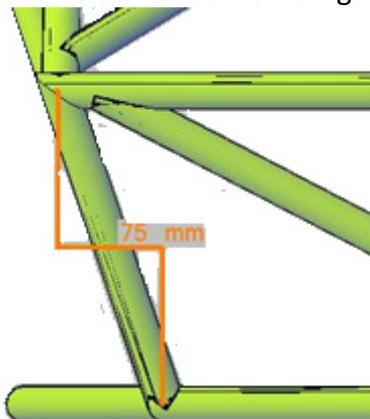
Vista frontal de la parte delantera derecha³⁴
